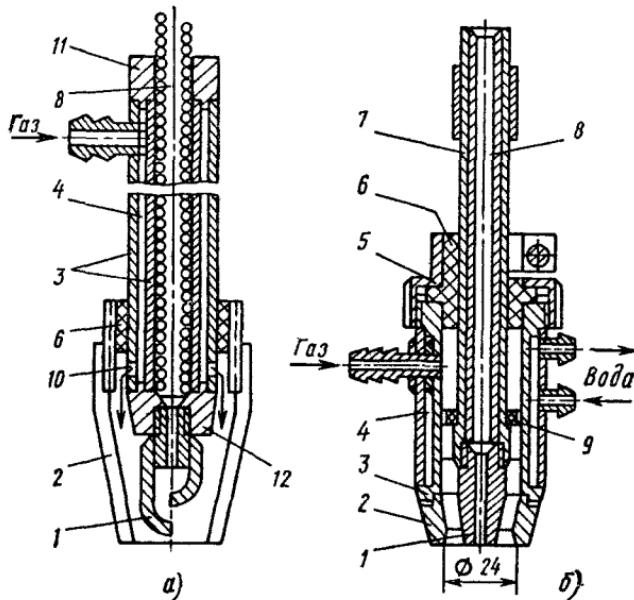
Горелки для сварки в CO_2 на малых (а) и больших (б) токах:
